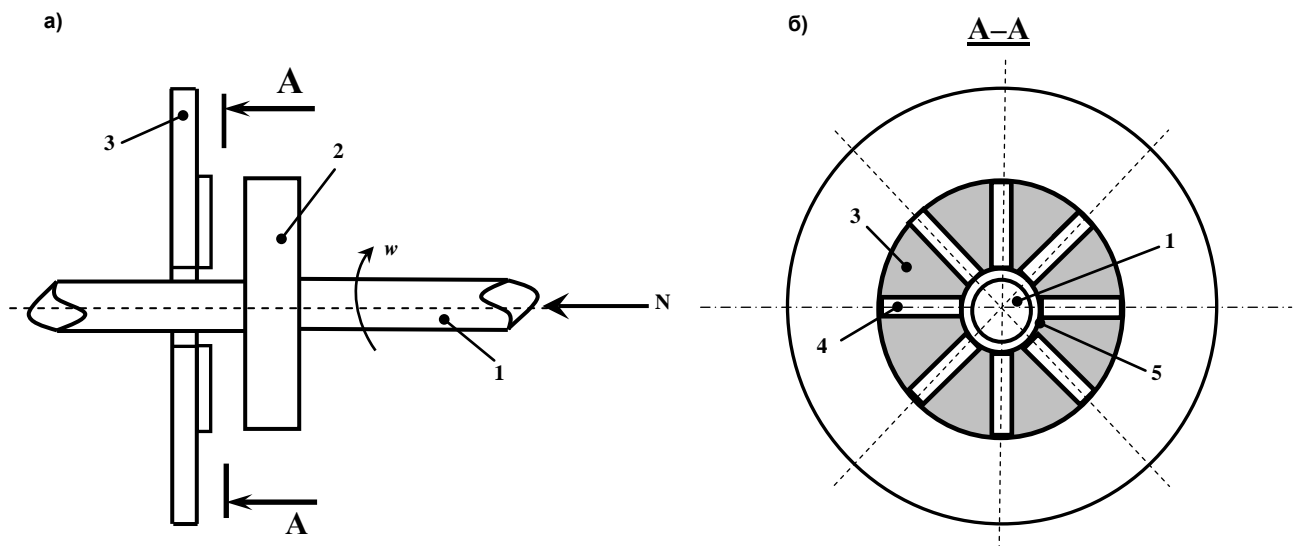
Схема упорного подшипника скольжения ТКР ДВС:
